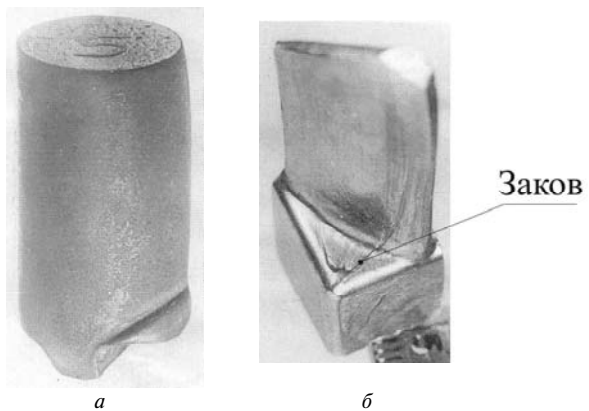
Образование закова на заготовке лопатки 5 ступени компрессора:
